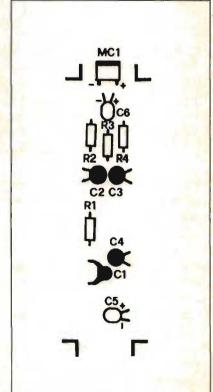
Circuito stampato cod. 890.66: montaggio dei componenti (lato B).
